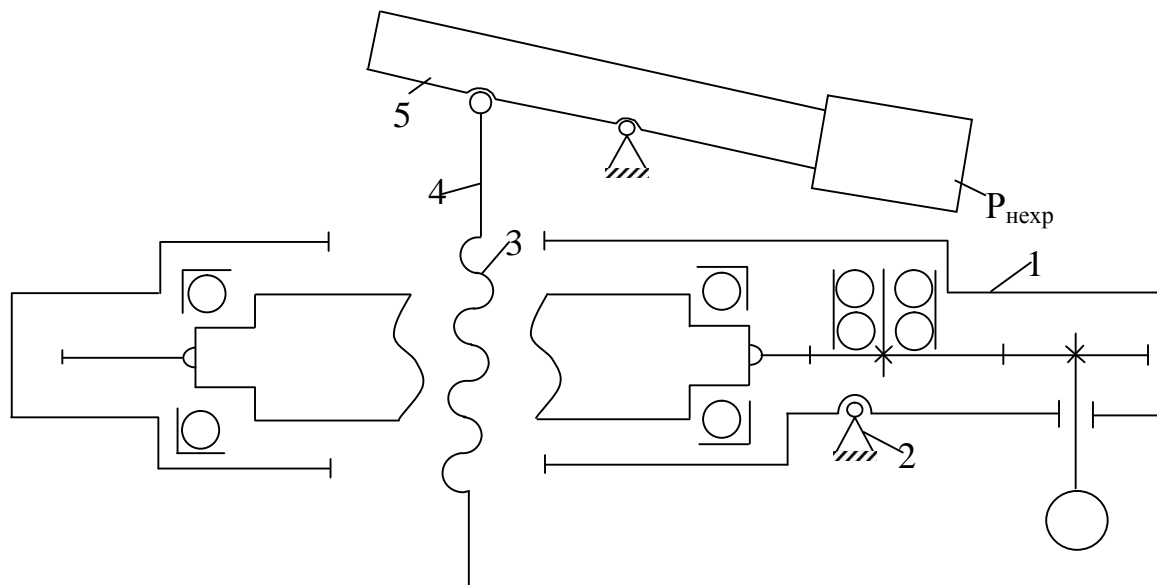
Схема исполнительного механизма линейного перемещения: 1 – корпус исполнительного механизма линейных перемещений; 2 – ось вращения корпуса; 3 – ходовой винт; 4 – шток; 5 – нагрузка; 6 – ось вращения нагрузки.
